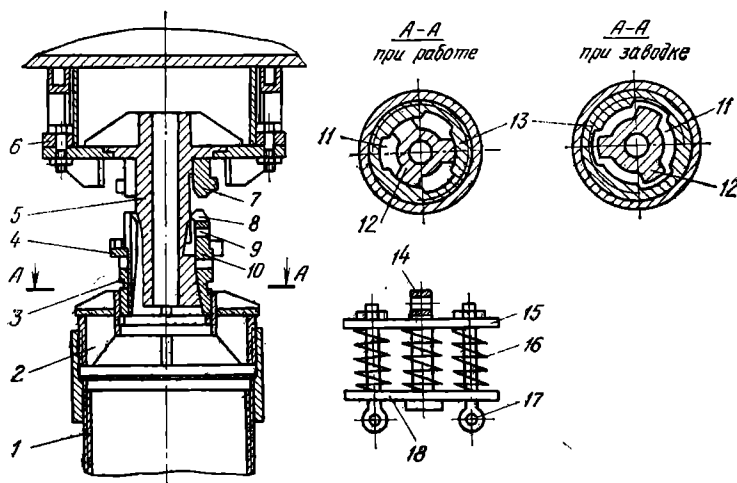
Самозаклинивающийся захват и амортизатор:
